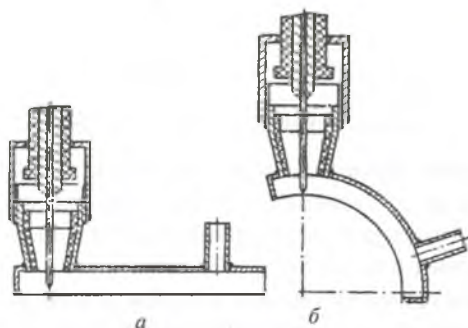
Конструкция «плавающего» сопла с козырьком для сварки продольных (а) и кольцевых (б) швов титано-алюминиевых соединений
